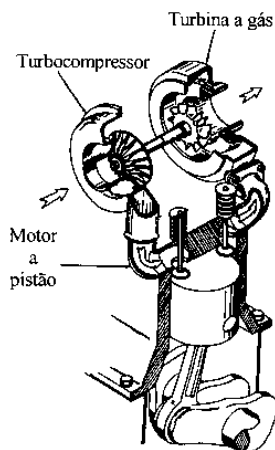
Turboalimentador de motor a pistão (Fonte: Schwitzer).
